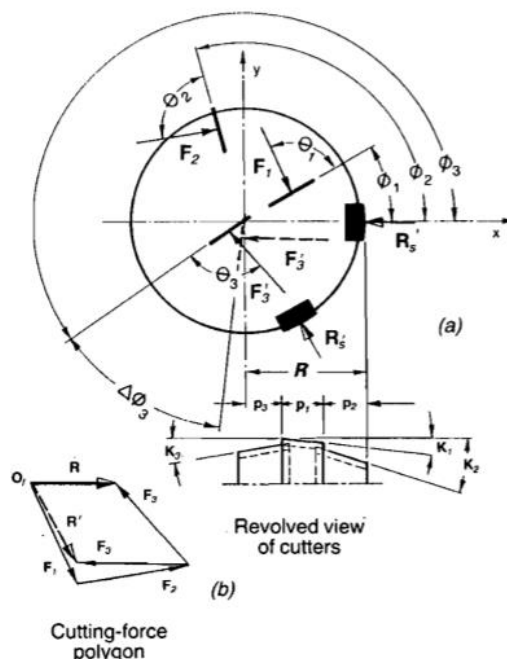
Твердосплавное сверло БТА с тремя режущими пластинами.
